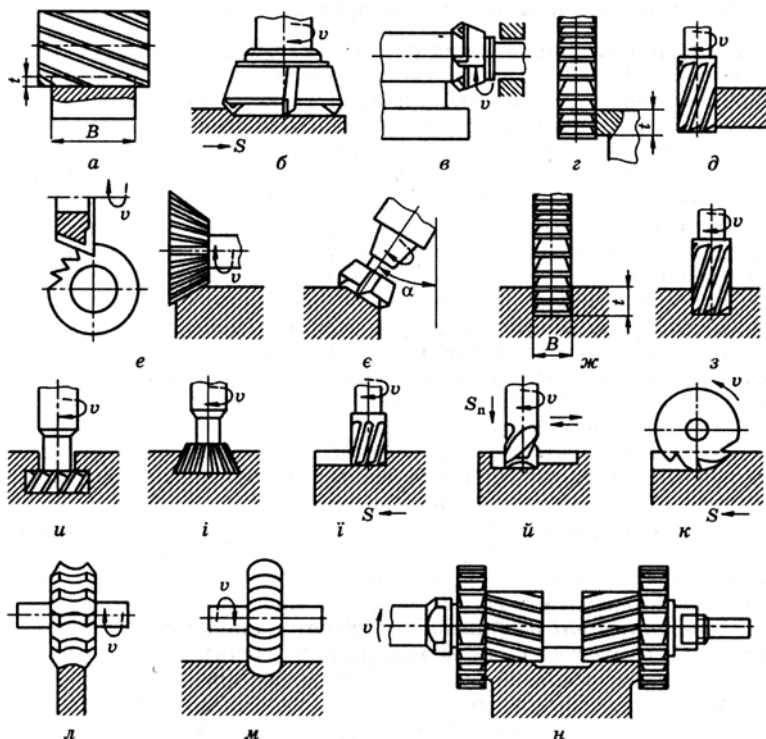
Приклади робіт, які виконують на фрезерних верстатах:
